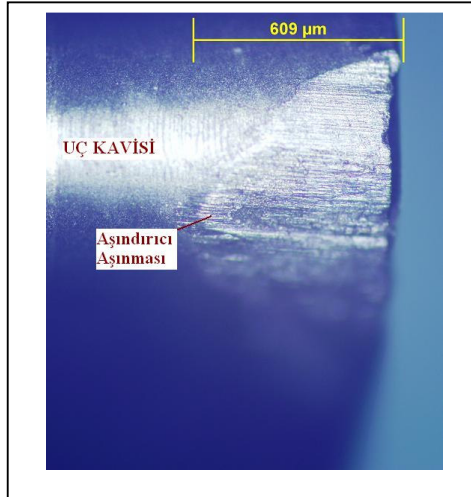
1.2738 plastik kalıp çeliğinin PCBN kesici takım ile işlenmesi neticesinde
